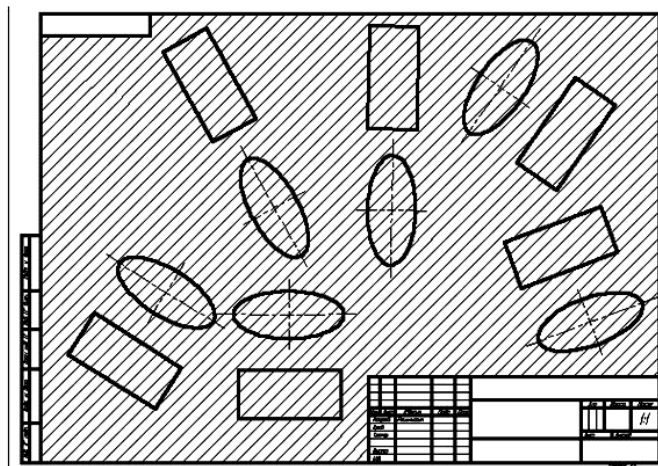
Направление штриховки под углом 45° к линиям рамки чертежа
